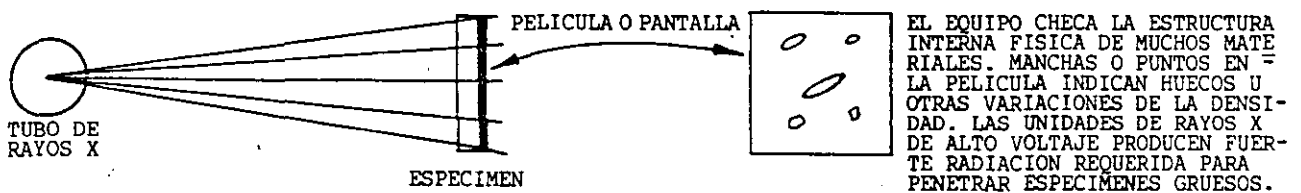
FIG. ESQUEMA DE UNA FOTOGRAFIA DE RAYOS X A UNA SOLDADURA.
